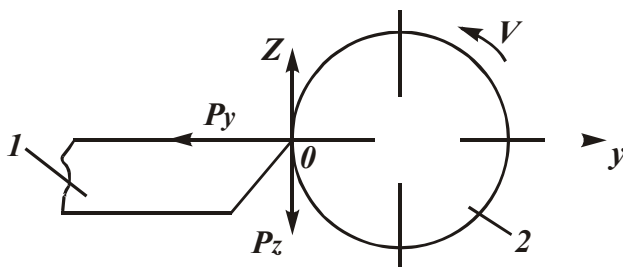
Расчетная схема: 1 – резец; 2 – обрабатываемая деталь.
